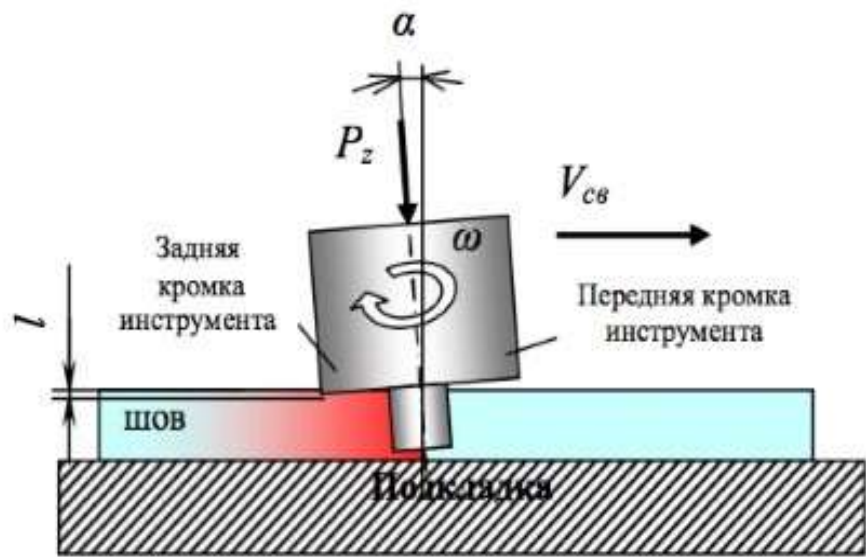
Принцип действия сварки трением с перемешиванием.
